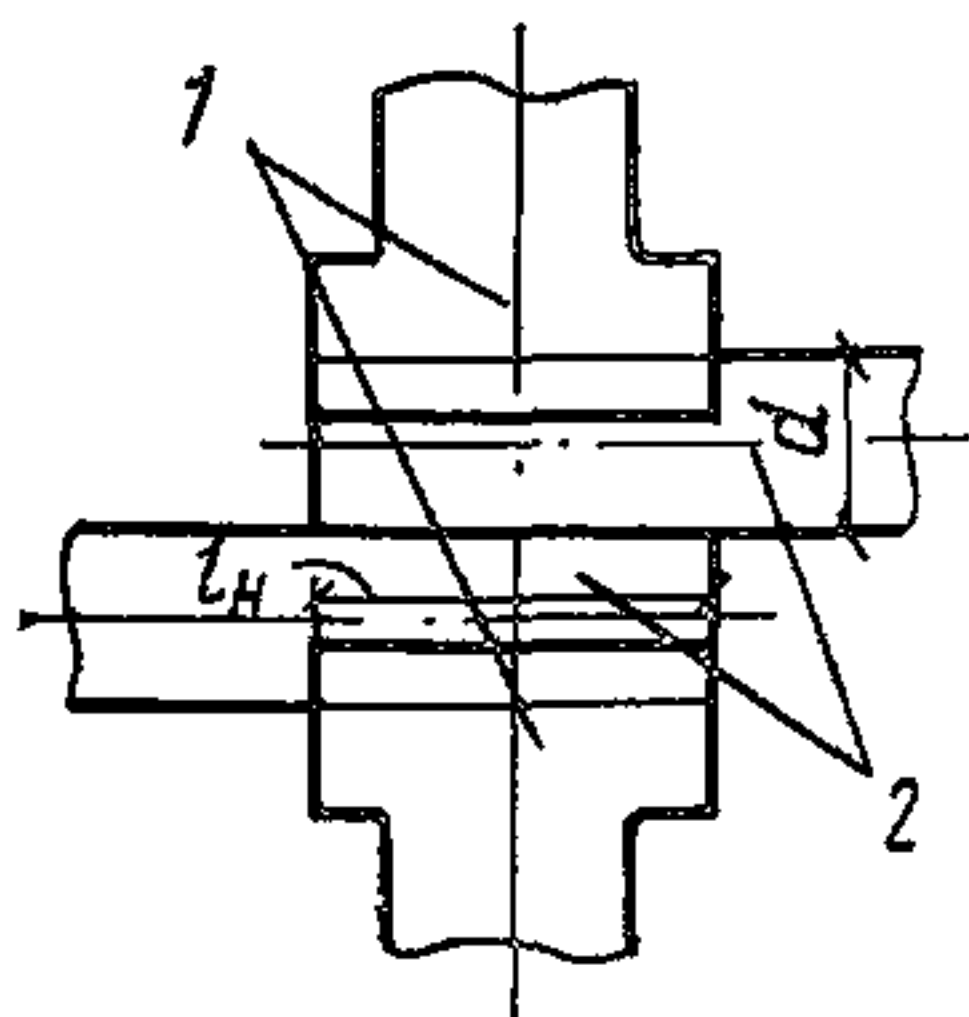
Схема подготовки и сборки концов стержней в электродах машины перед сваркой внахлестку
